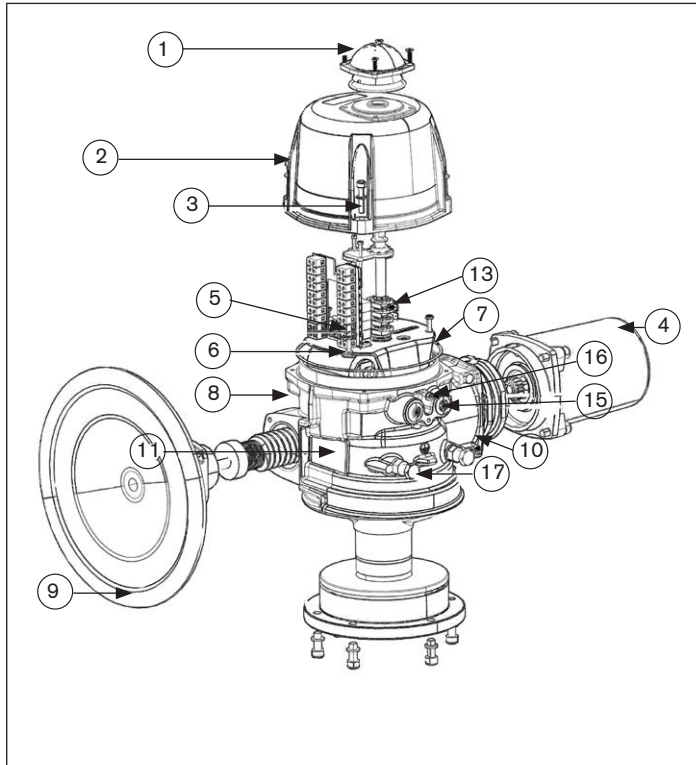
Explosionsdarstellung Motor 600 - 1000 Nm
